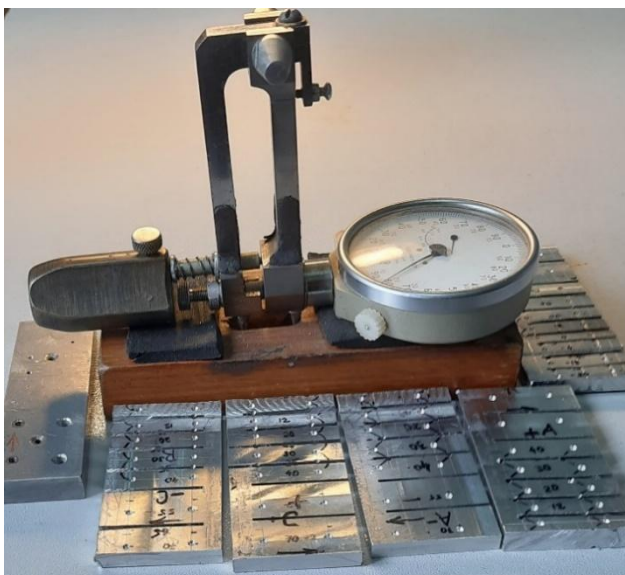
Зовнішній вигляд механічного деформометра, база вимірювання 20 мм, та вирізані частини зварного зразка (темплети) з матеріальними базами (конусні отвори) для визначення ЗЗН
